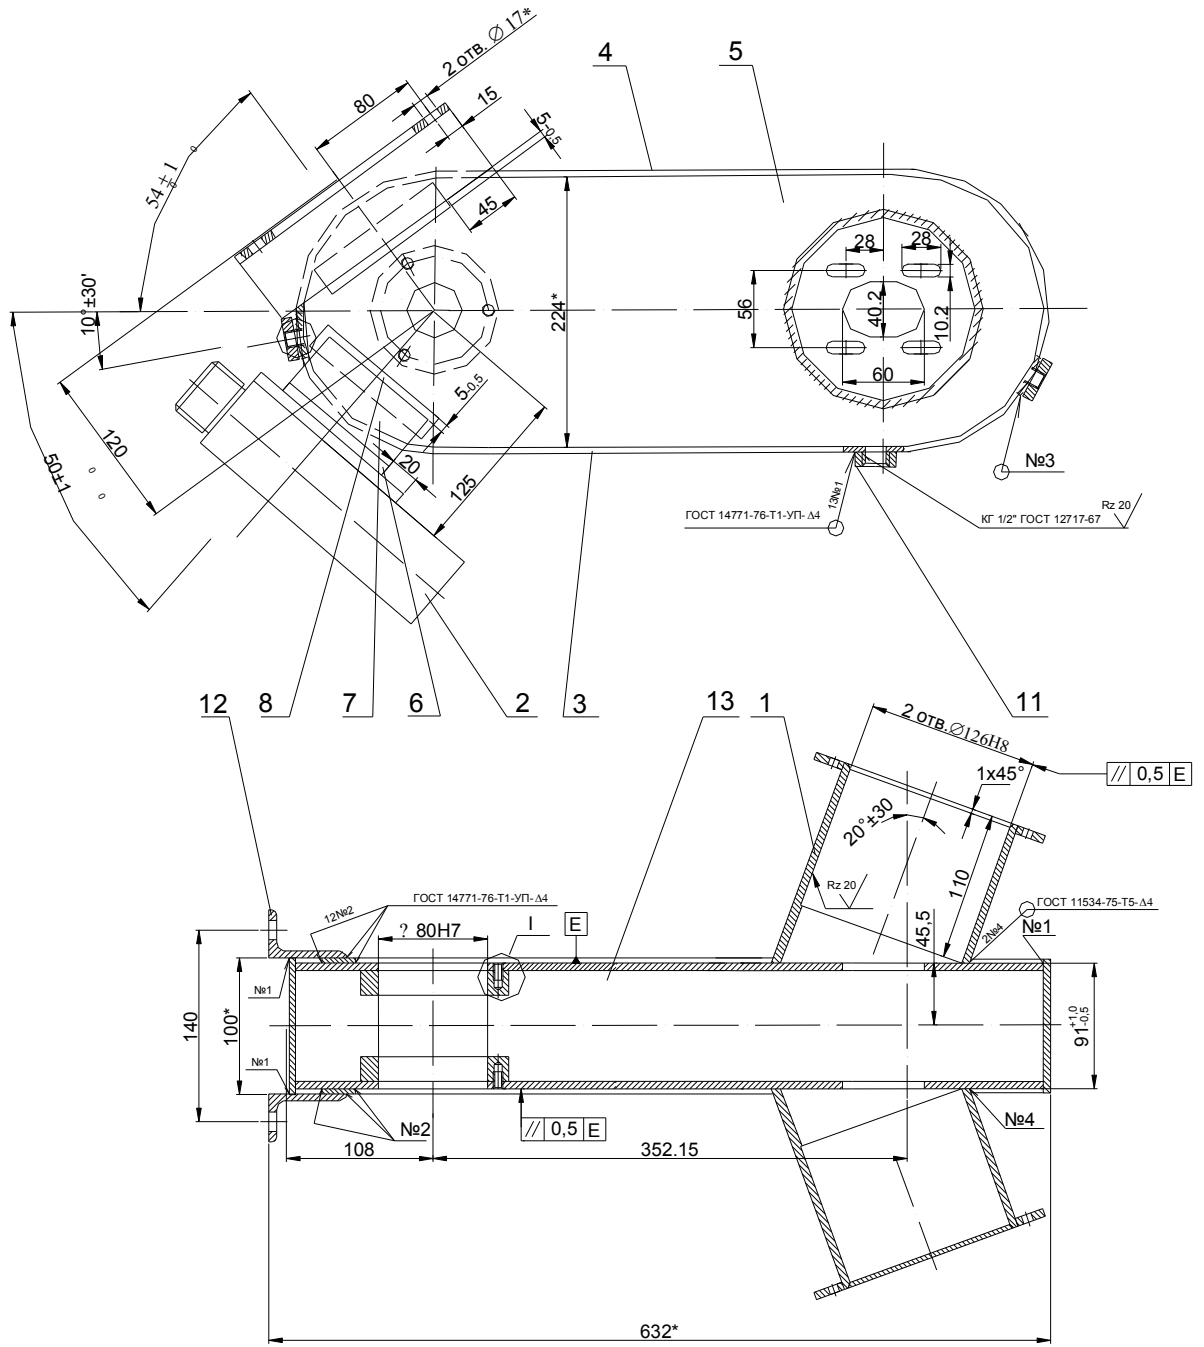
Варіант модернізованого корпусу редуктора
